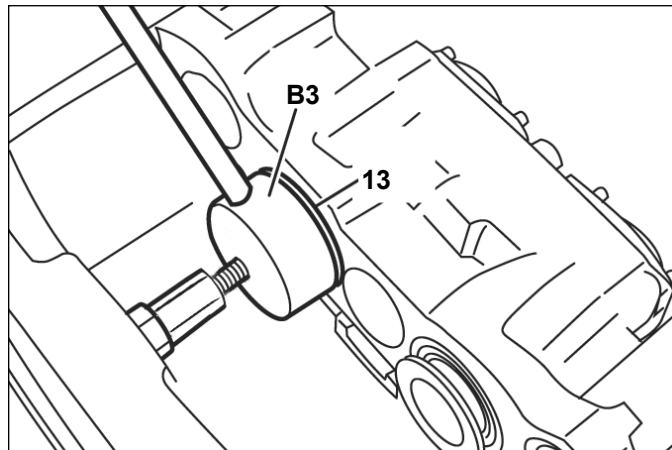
INSTALLATION DU POUSSOIR ET DU CACHE-POUSSIÈRE HORS VÉHICULE
